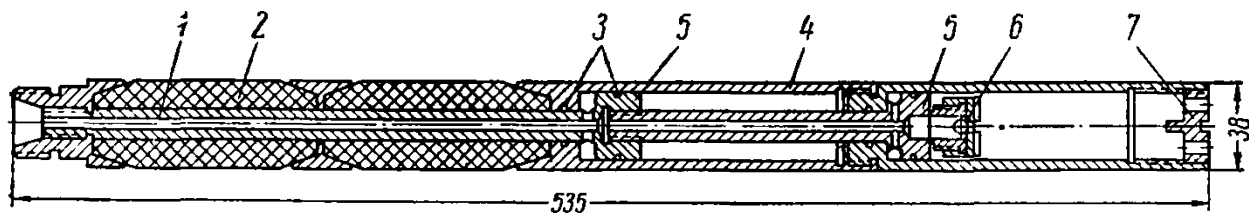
Гидрозатвор автоматический типа АГ-3А:
